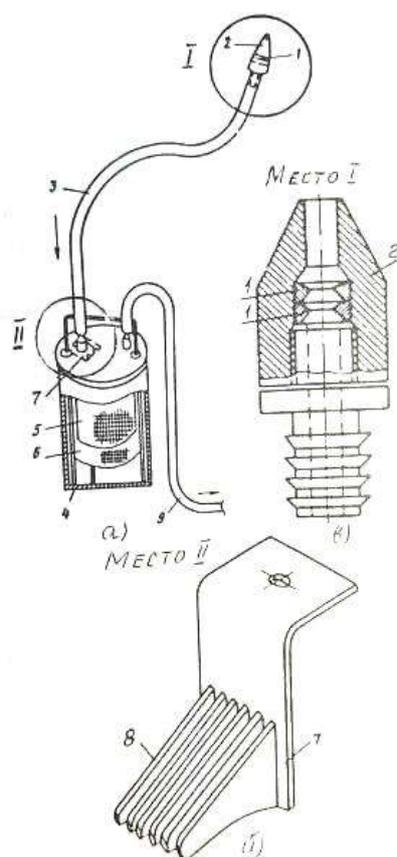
Схема аппарата для съема ягод облепихи (а), приспособления для дробления ягод (б) и пневматической насадки (в);
